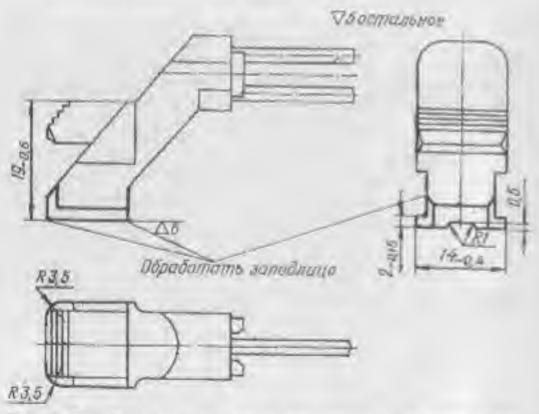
Обработка выступов пятки папривляющей возаразной пруживы после наплавки
